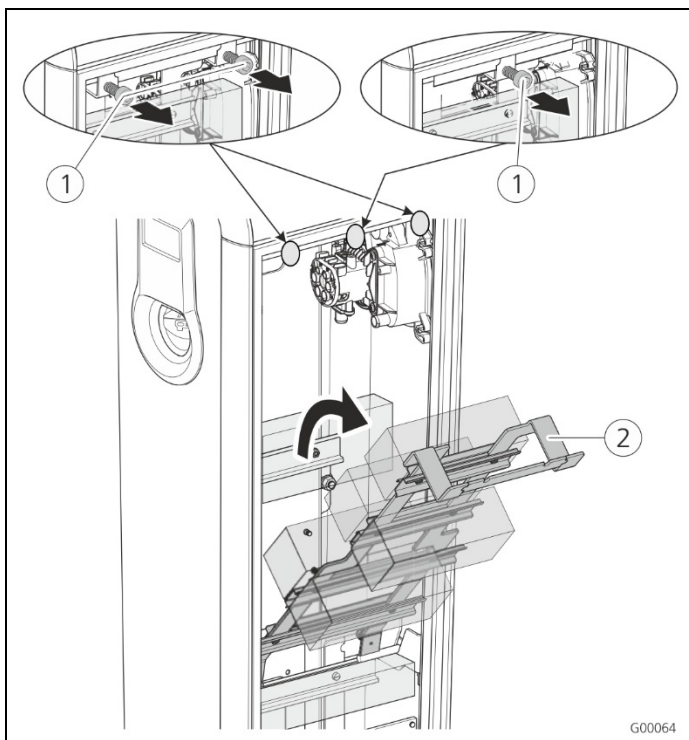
Schwenkrahmen ausklappen (Beispiel)
